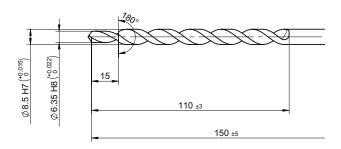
Stufenbohrer Typ 1337A2 für Montagenippel 3/8-24 UNF
